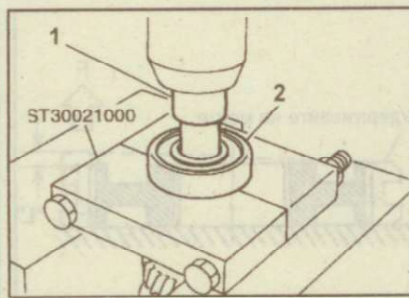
Использование прессы и оправки (1) для снятия заднего подшипника (2) с первичного вала
